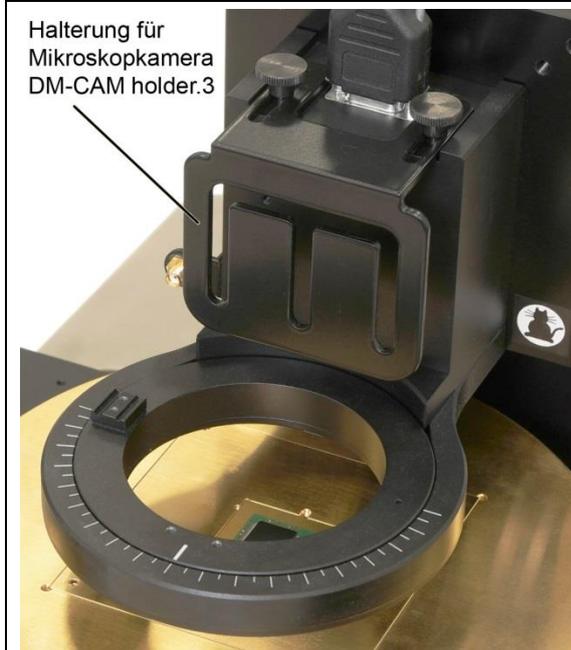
Befestigter Kamerahalter DM-CAM holder.3
